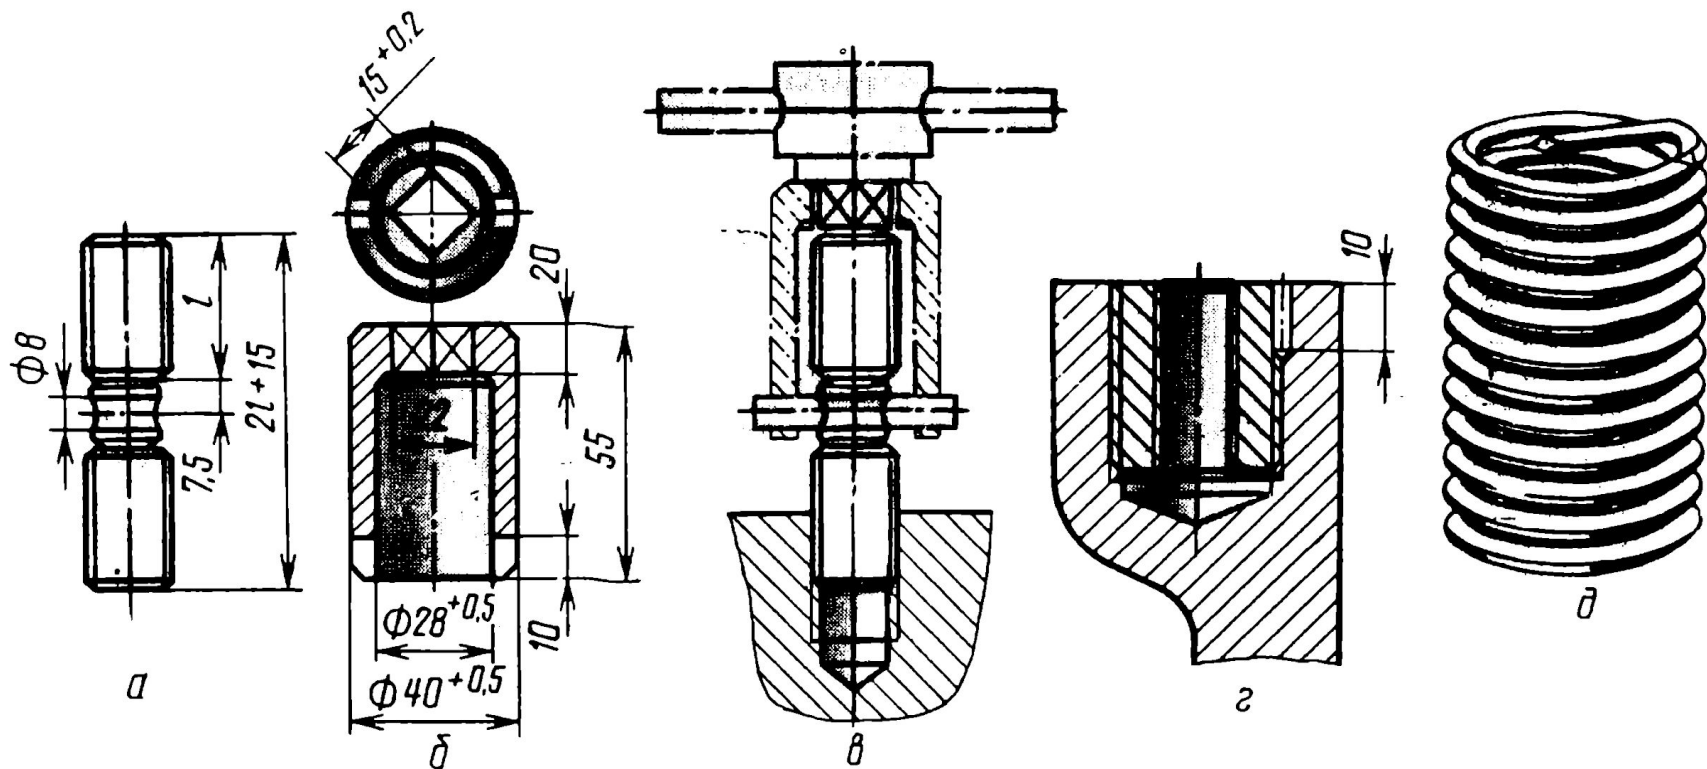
Восстановление резьбы постановкой дополнительной детали:
